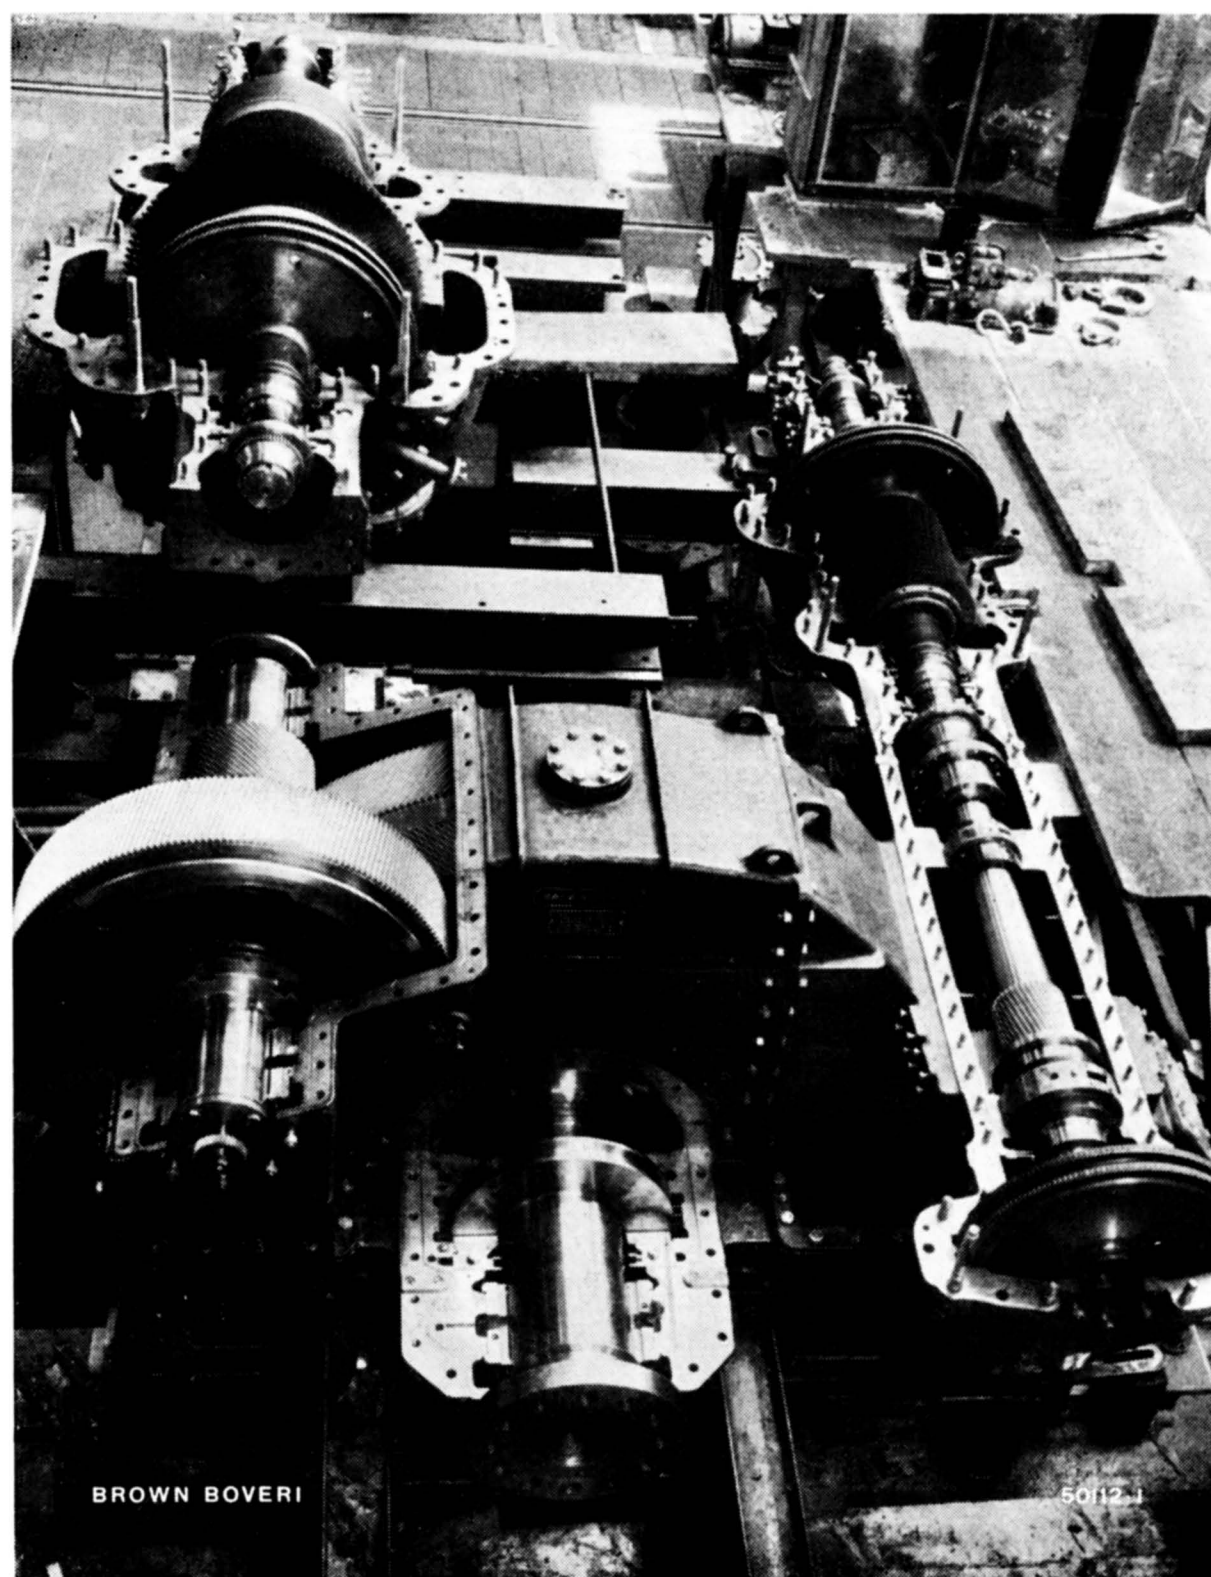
Groupe de turbines à engrenages pendant son montage à la plate-forme d'essais.
